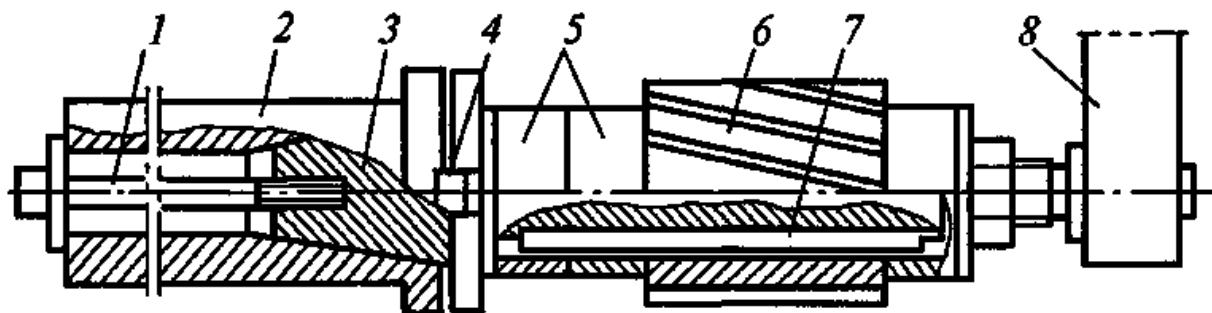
Установка цилиндрической фрезы на длинной оправке:
